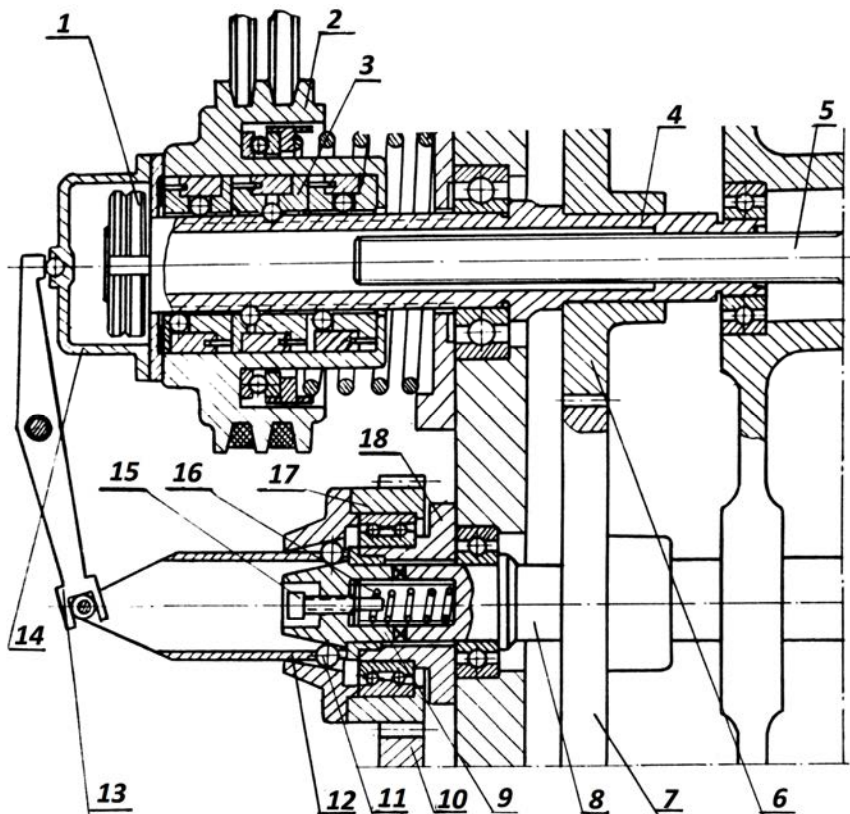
Конструкція передаточного механізму привода свердлильного верстата з адаптивним управлінням
